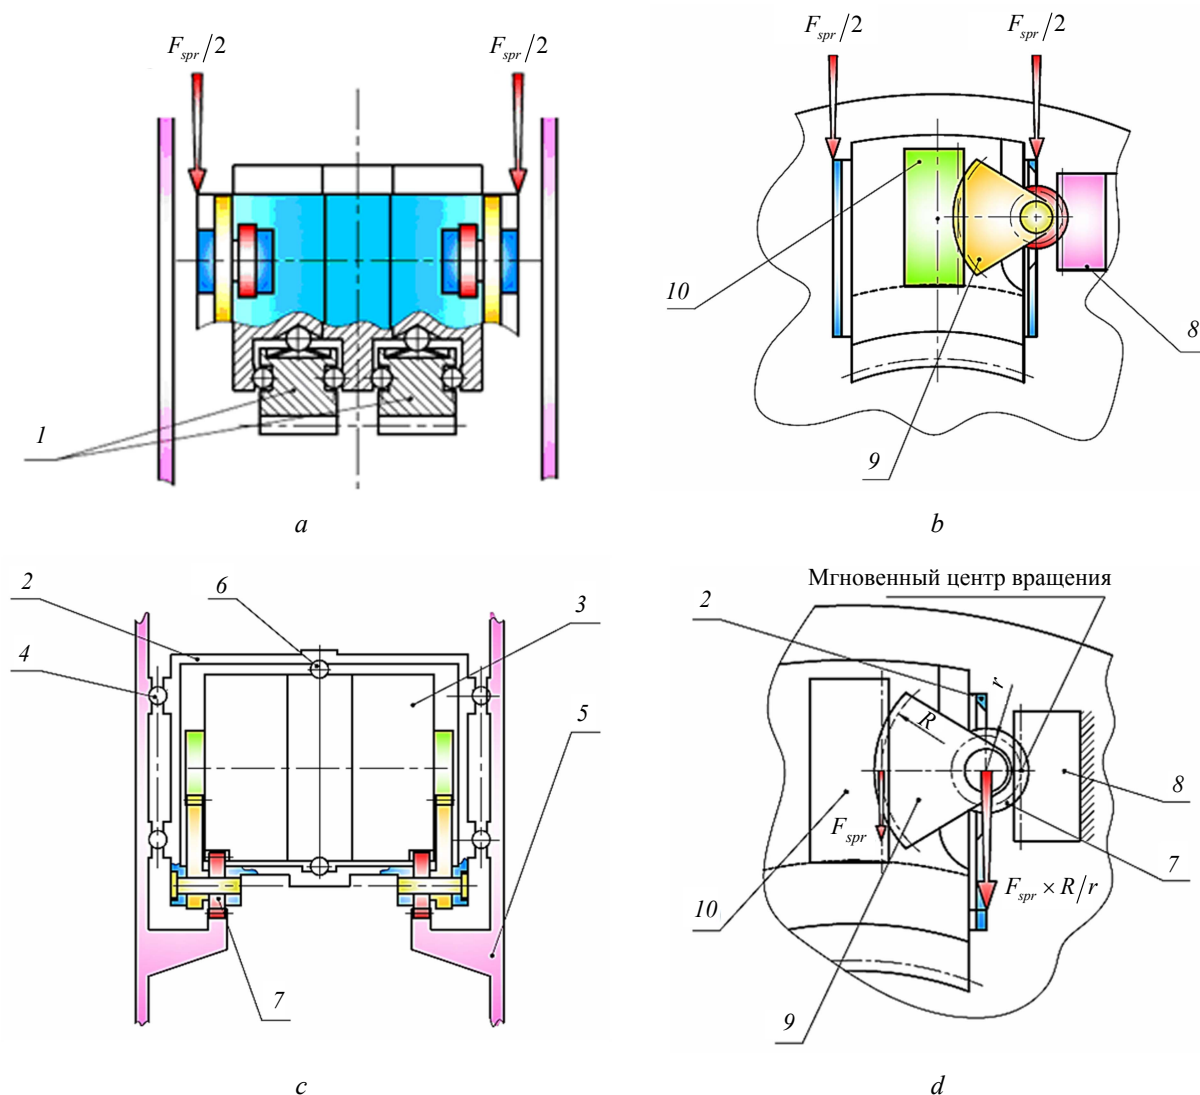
Вариант конструкции корпуса двухпоточного сектора центрального зубчатого колеса: *a-c* – вид спереди, сбоку и сверху соответственно; *d* – расчетная схема
